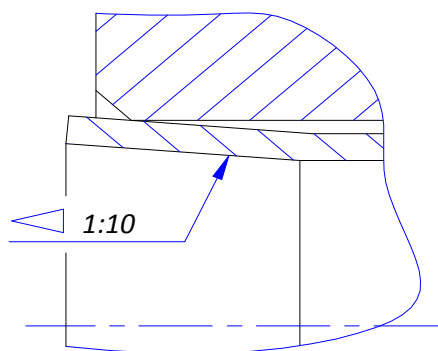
Конічне розвальцювання труби перед зварюванням
